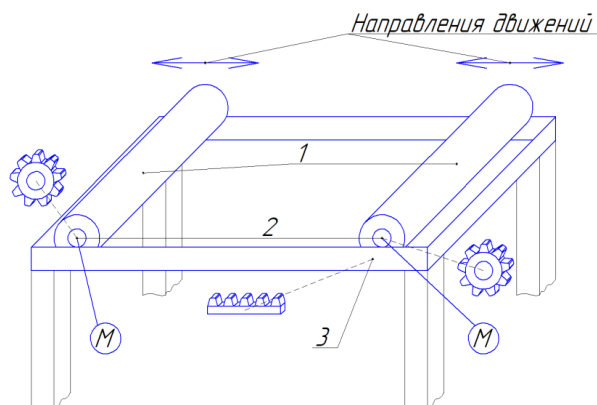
Общая схема конструкции разравнивающего устройства
